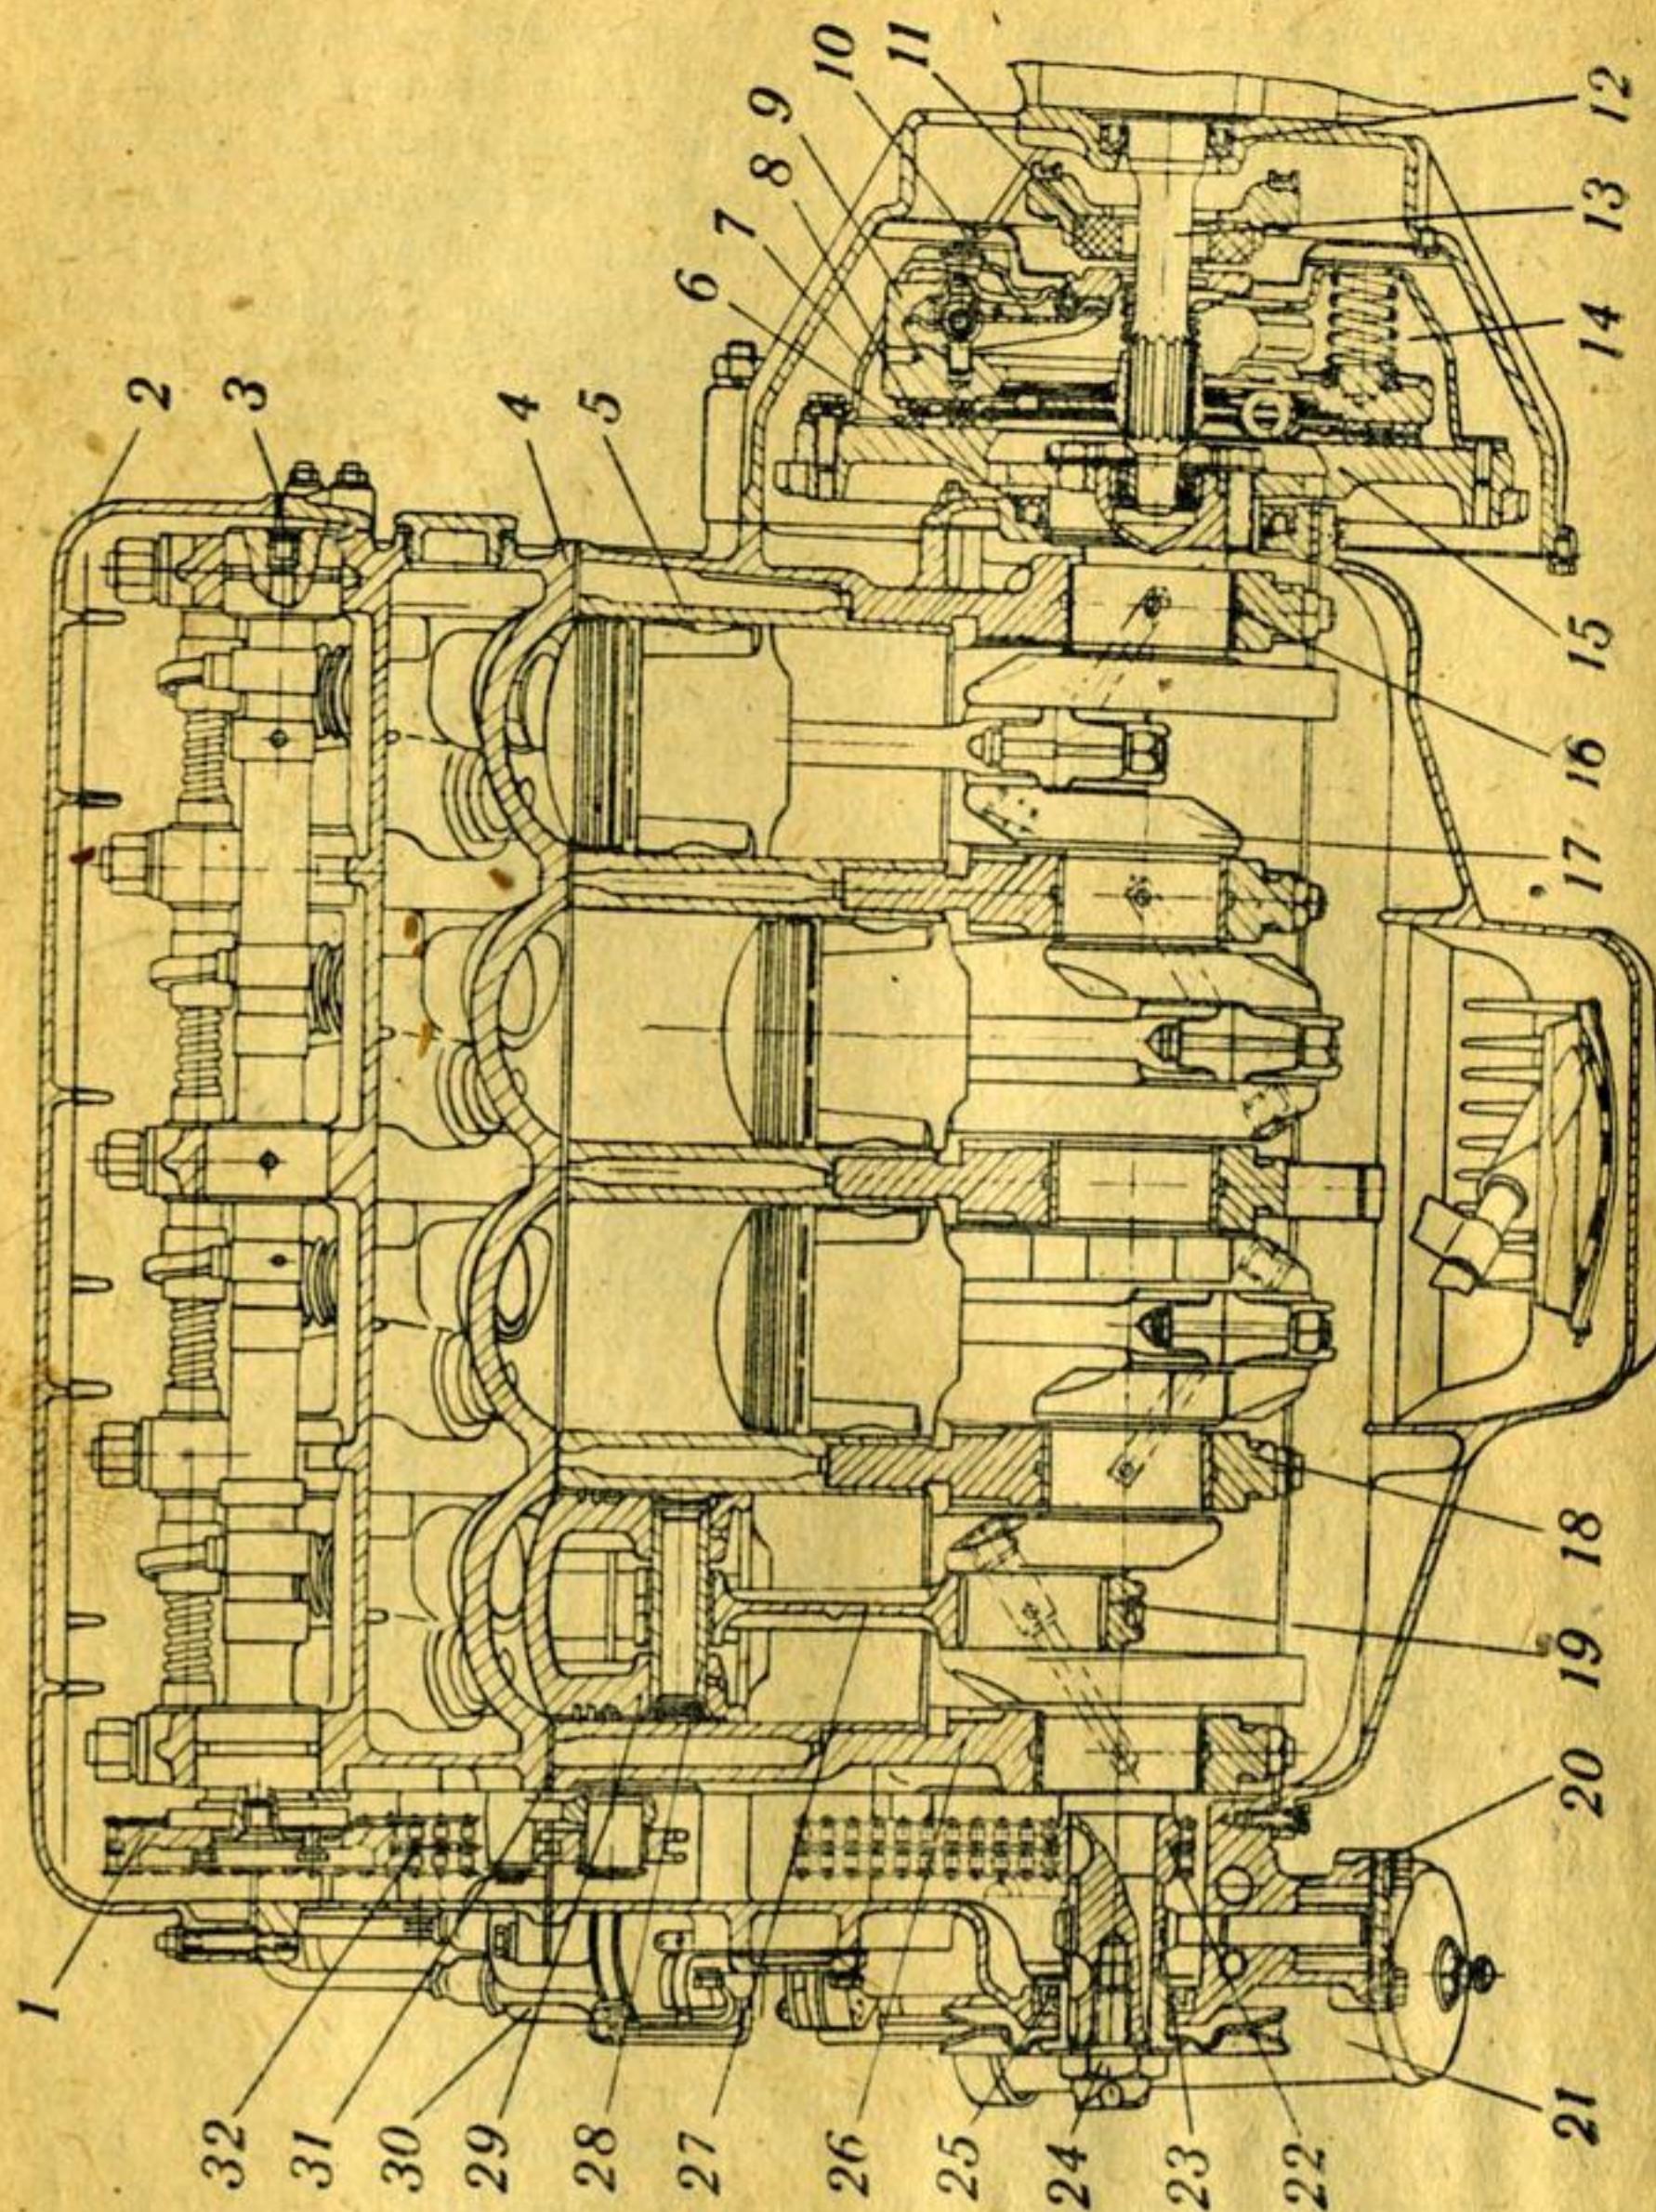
Продольный разрез двигателя «Москвич-412»:
